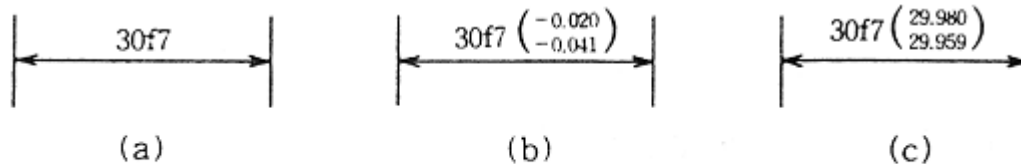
공차역 클래스에 의한 치수허용차의 기입법
